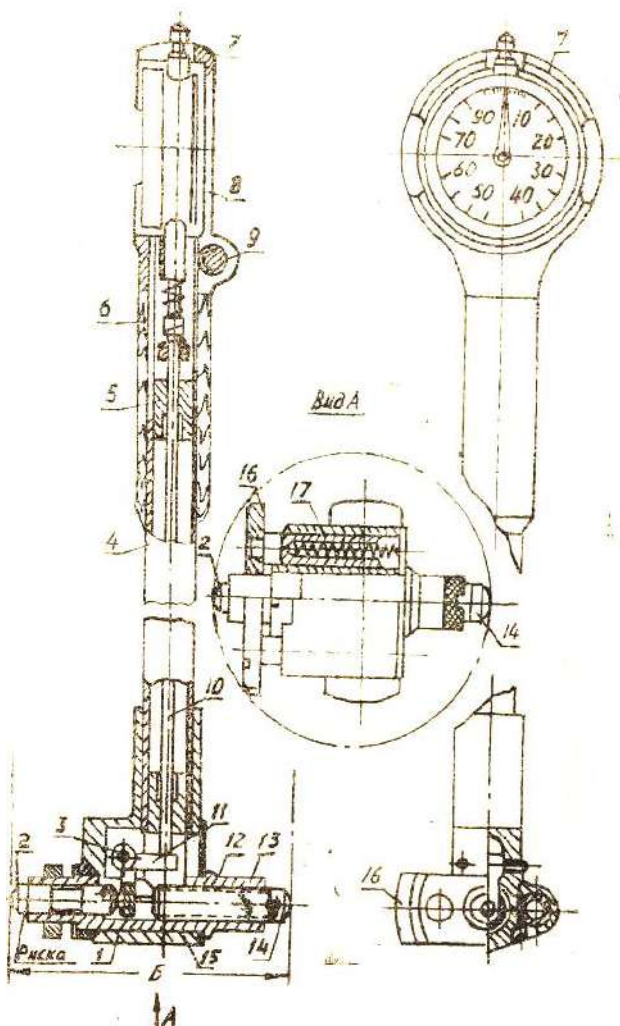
Индикаторный внутренний измеритель (с рычажной передачей). 1-шар; 2-подвижный стержень; 3-ремень (ось); 4-патрубок; 5-теплонепроницаемый ряд; 6-пружина; 7-кожух; 8-индикатор; 9-стопорный винт; 10-стержень; 11-двухколенный рычаг; 12-втулка; 13-стопорная гайка; 14-сменный стержень; 15-корпус; 16-центрирующий мостик; 17-пружина.
